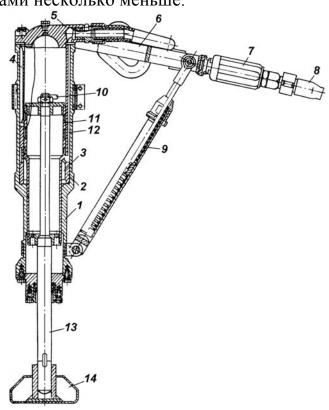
Пневматическая трамбовка: 1 – корпус; 2 – ствол; 3 – кольцевая полость; 4 – канал; 5 – крышка; 6 – рукоятка; 7 – пусковое устройство; 8 – воздушный шланг; 9 – амортизатор; 10 – отверстие; 11 – поршень; 12 – канал; 13 – шток; 14 – трамбующий башмак
